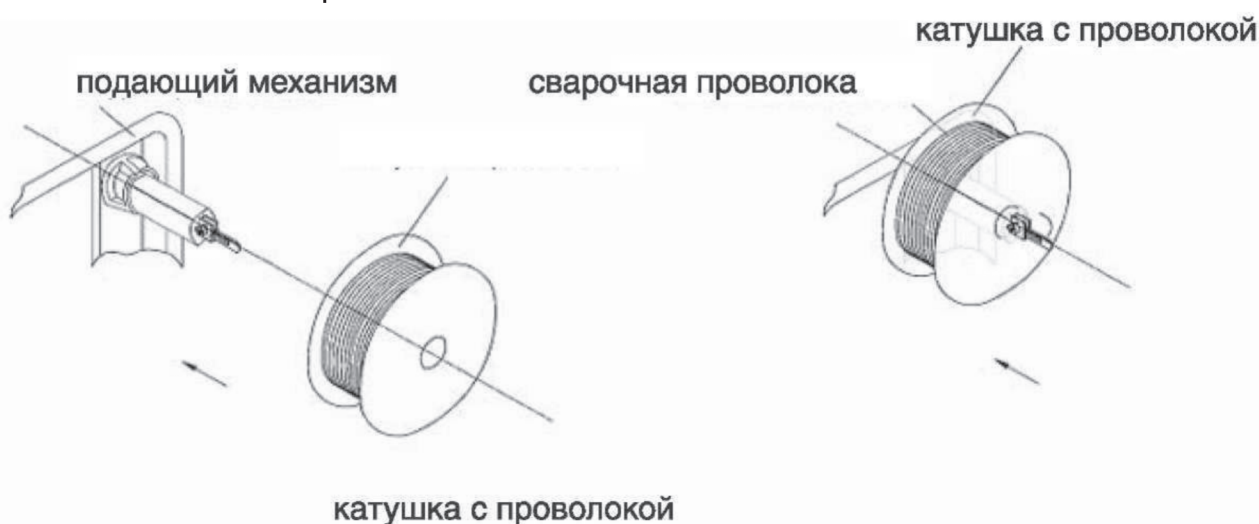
Установка кассеты со сварочной проволокой
